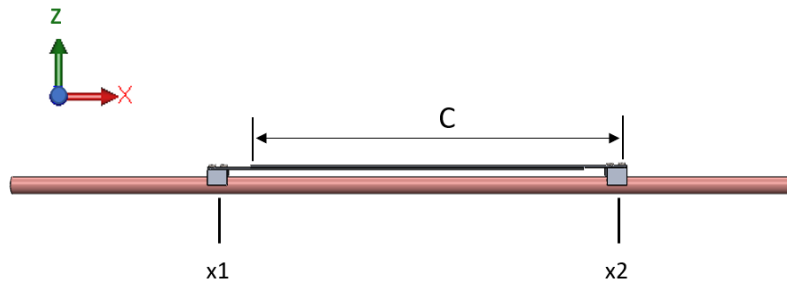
Deslocação do sistema longitudinalmente (variação do comprimento da viga e posicionamento das abraçadeiras)
